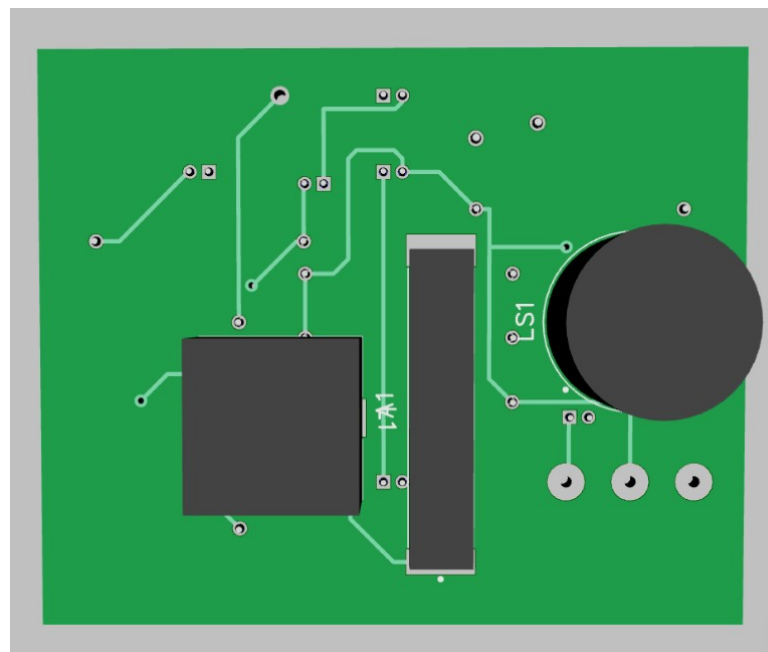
3D модель печатной платы. Вид со стороны Б
